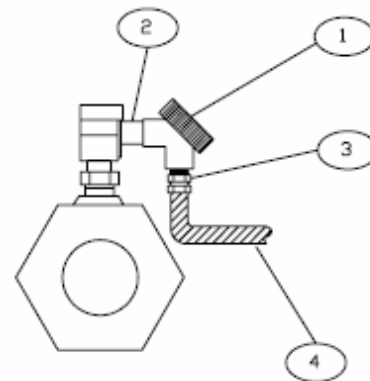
9 Válvulas operadas con solenoide en la planta X-1602
